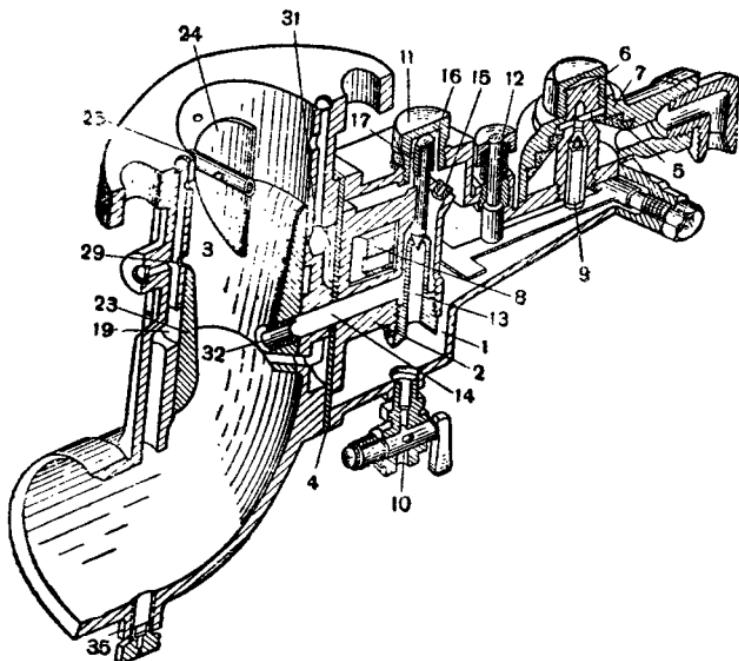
Разрез карбюратора двигателя ЧТЗ.
